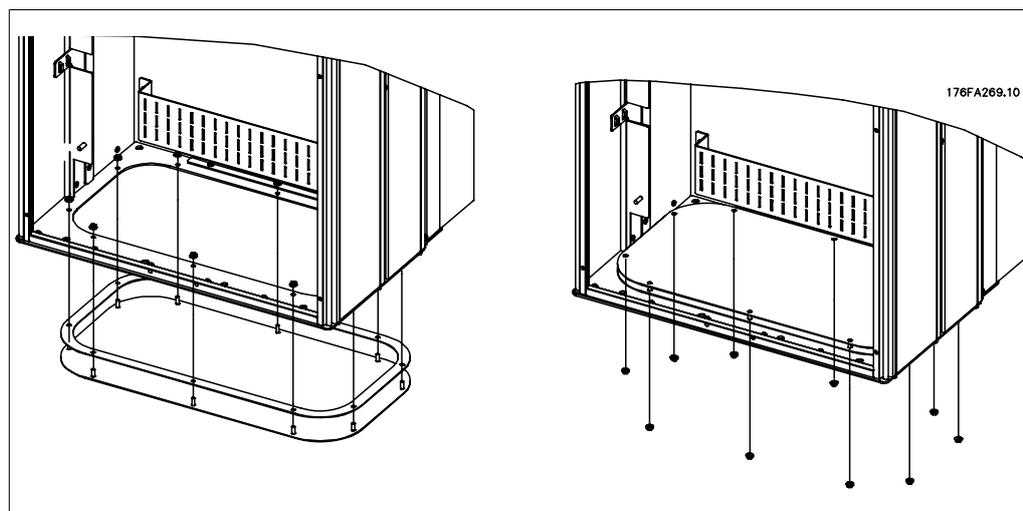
Befestigung des Bodenblechs, Gehäuse E1
